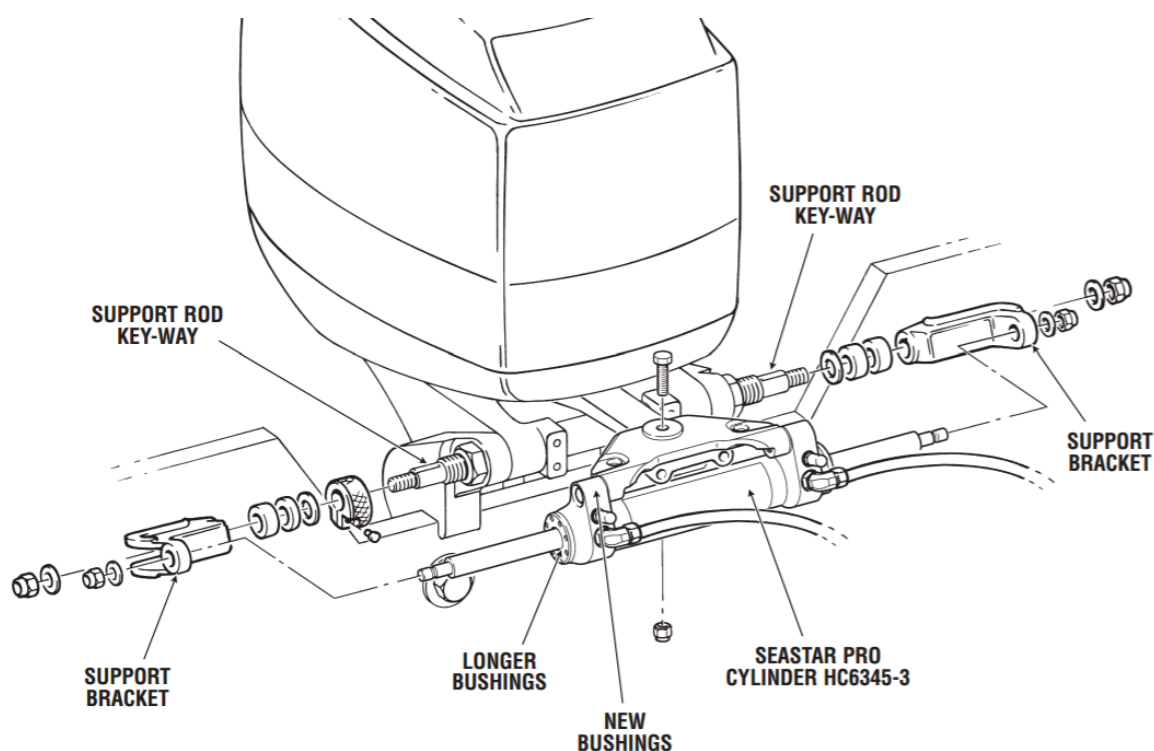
explosión de un mecanismo de dirección de motor con cilindro único de doble efecto. Fuente [3]
